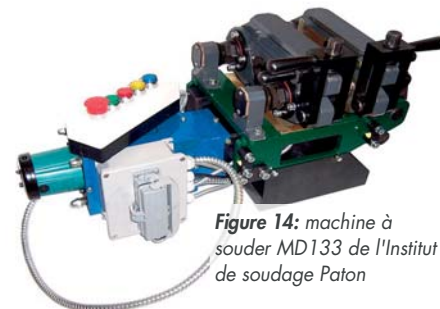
machine à souder MD133 de l'Institut de soudage Paton
